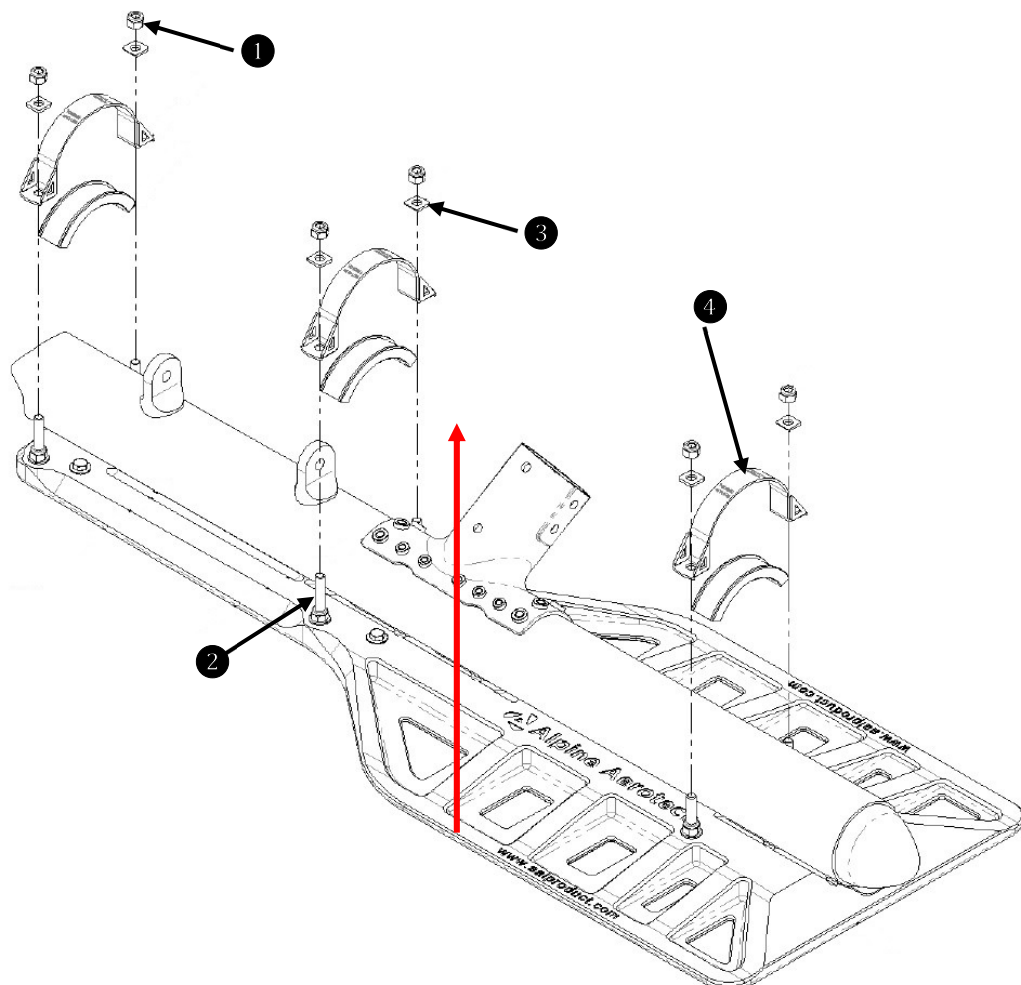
Montage-Zeichnung des *bear paw* mit Befestigungsmutter ①, Schraube ②, Unterlegscheibe ③ und Befestigungslasche ④. Der rote Pfeil bezeichnet diejenige Stelle, an der die Kraft zum Drehen eines *bear paw* um die Längsachse der Kufe gemessen wurde. Quelle: ICA des STC-Halters.
